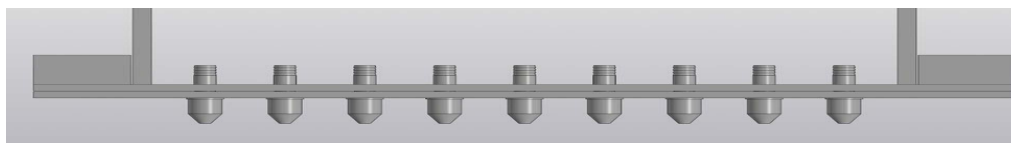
3D-модель пластины с дозаторами и пневмоцилиндрами
